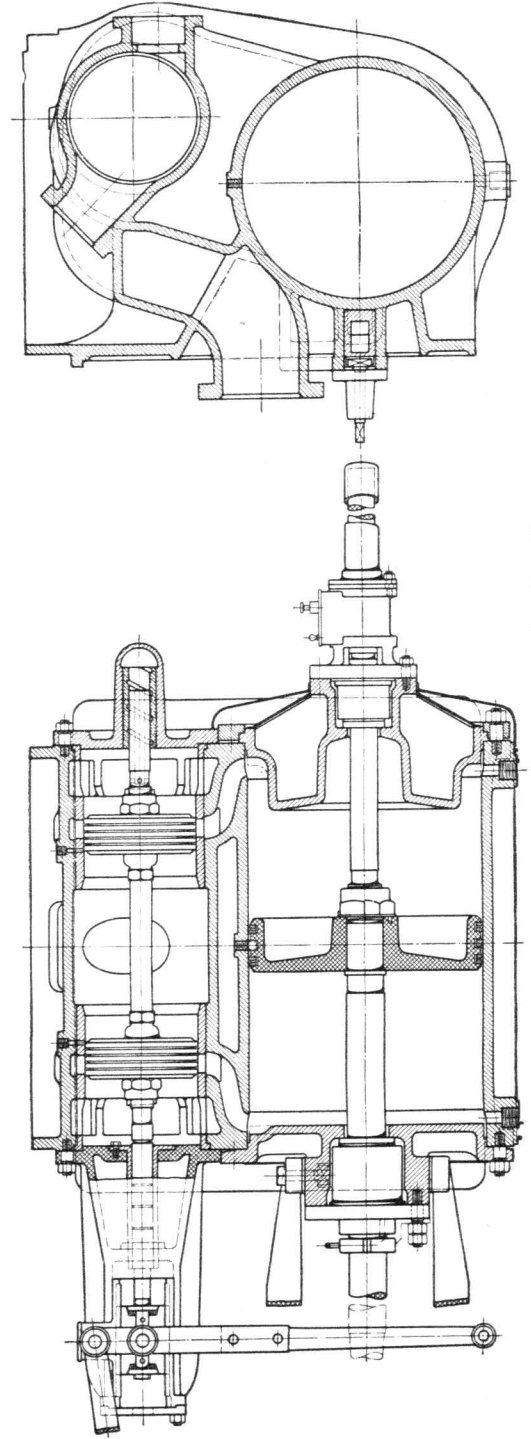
Dampfzylinder und Kolbenschieber mit federnden Ringen.
